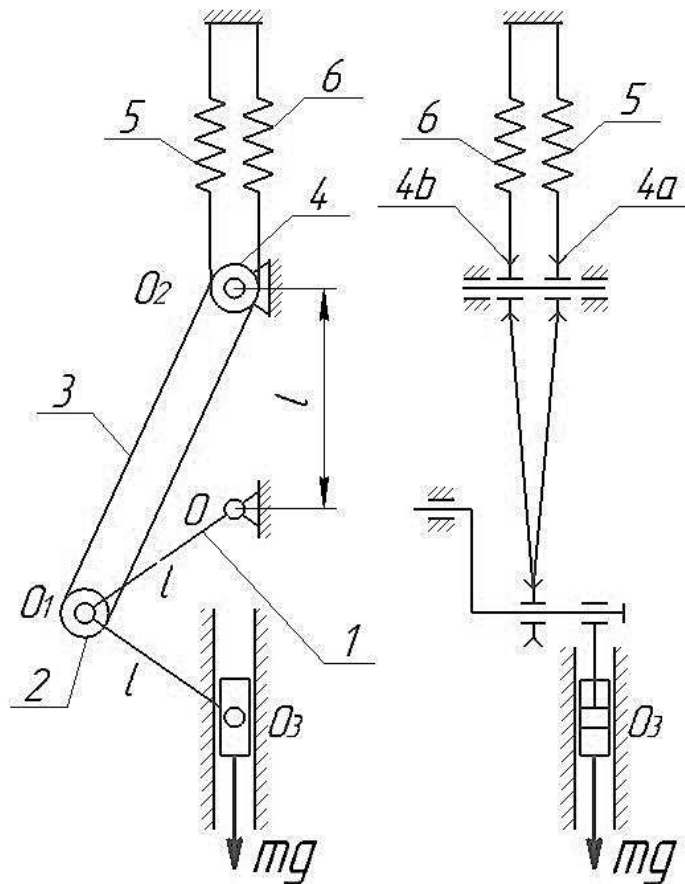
Схема уравновешивающего устройства для привода штангового глубинного насоса: 1 – поворотный рычаг, 2 – блок, 3 – гибкий элемент, 4а, 4б – блоки, закрепленные на основании, 5,6 – пружины
